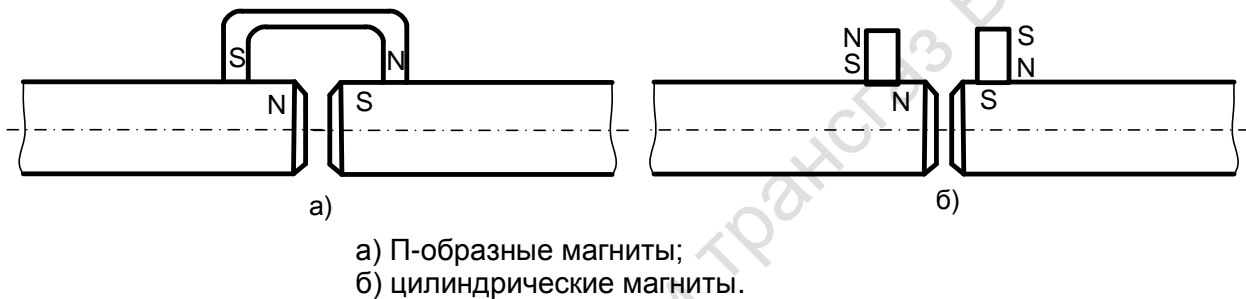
Схема размагничивания сварных соединений постоянными магнитами
